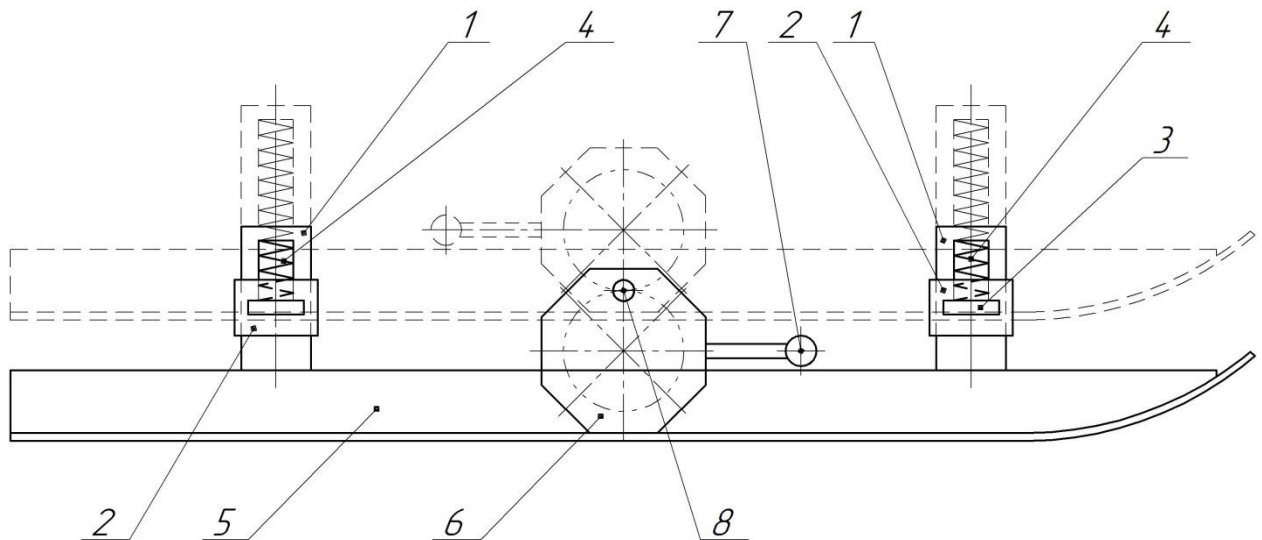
Опорна лижа з ексцентриковим механізмом регулювання глибини ходу сошника: 1 – вуха кріплення; 2 – кронштейн; 3 – упори; 4 – пружина; 5 – опорна лижа; 6 - ексцентрик; 7 – важіль; 8 – вал
